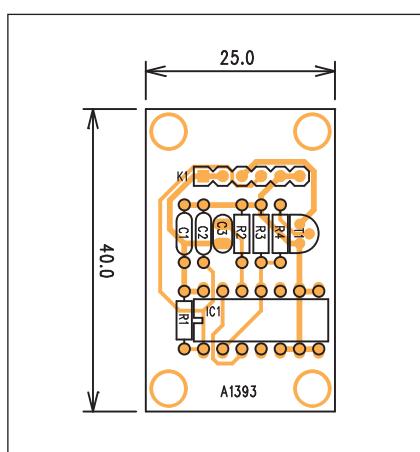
Obrazec desky spojů monitoru (strana BOTTOM)
